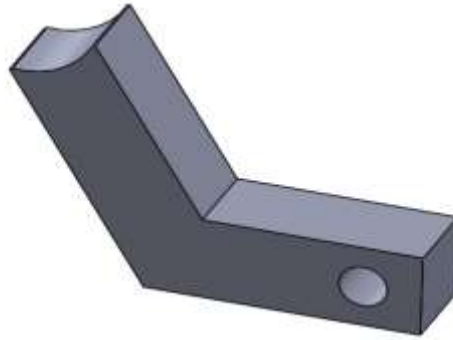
Base del tren de llantas parte inferior de la estructura
